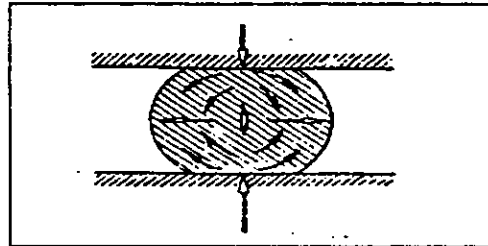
Formación de grietas en el proceso de barrenado por laminación.(2.16)
